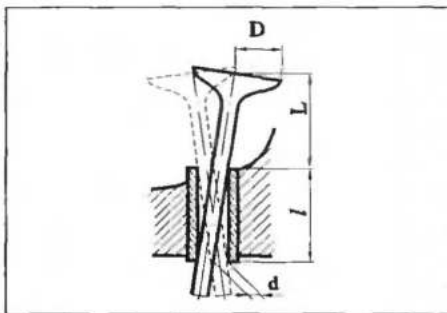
Схема косвенного измерения зазора между стержнем клапана и направляющей втулкой по люфту клапана во втулке: D — люфт тарелки; d — зазор во втулке; L — расстояние от втулки до тарелки; l — длина втулки
